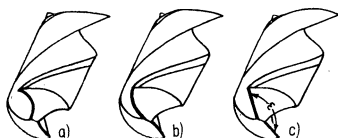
Falscher Bohreranschliff mit rückgewölbter Hauptschneide (a) oder vorgewölbter Hauptschneide (b), richtiger Bohreranschliff mit gerader Hauptschneide und richtigem Spitzenwinkel (c)
